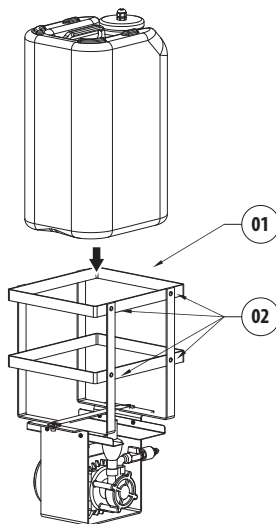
Réservoir 23l, hauteur de remontée d'eau de 30m.
